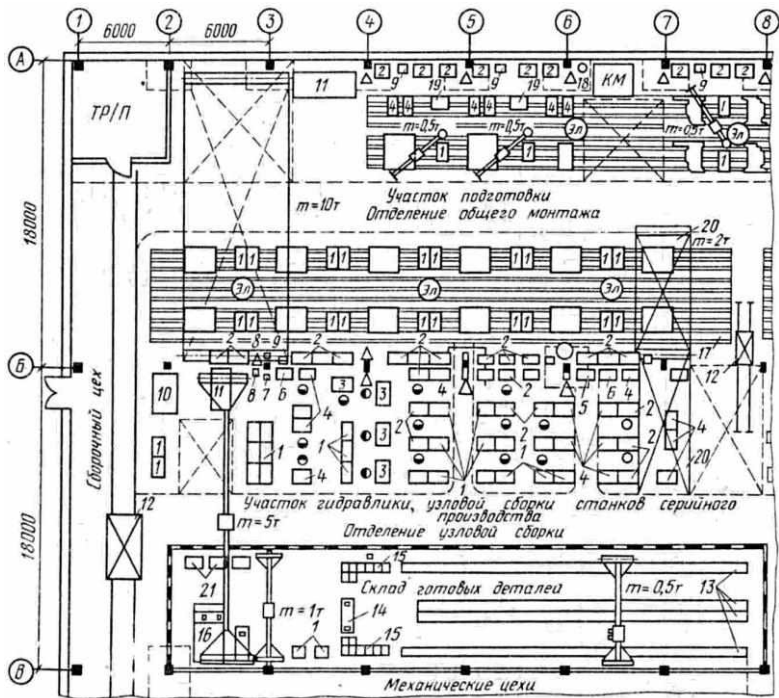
Планировка оборудования и рабочих мест сборочного цеха шлифовальных станков [1]
